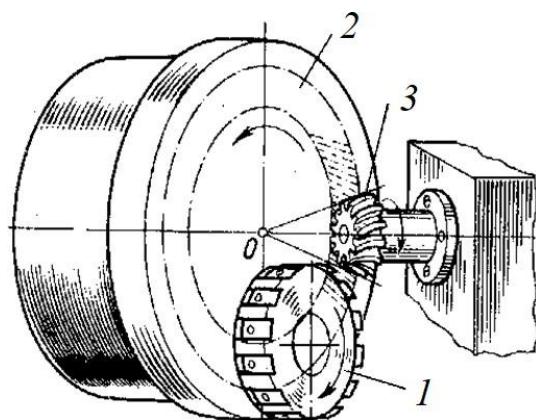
Схема нарізування конічного колеса з круговими зубцями [34]
